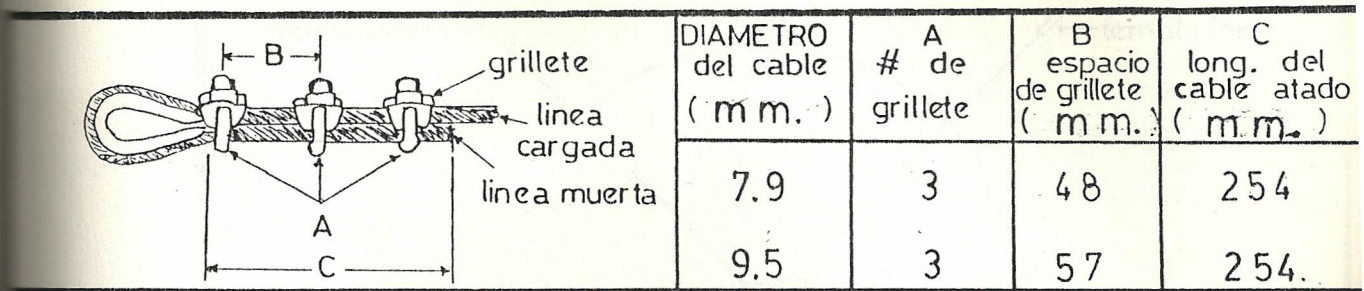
ESPECIFICACIONES PARA INSTALACION DE GRILLETES DE CABLES.
